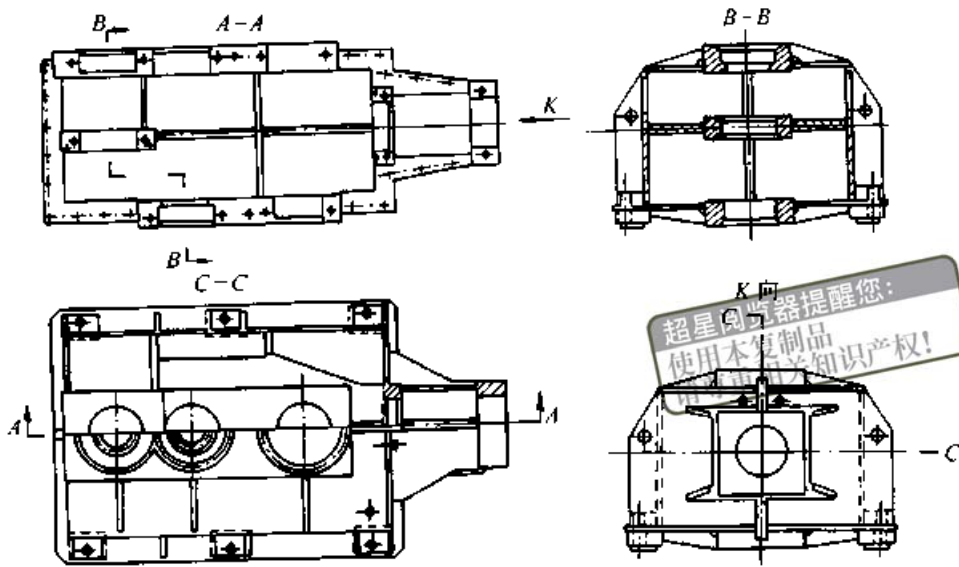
焊接结构的锥齿轮减速器箱体
